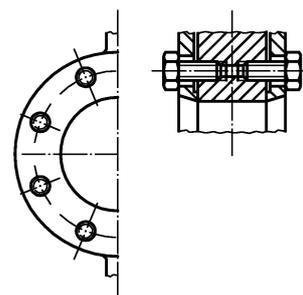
Einklemmklappe mit Monoflansch und Gewindebohrungen
